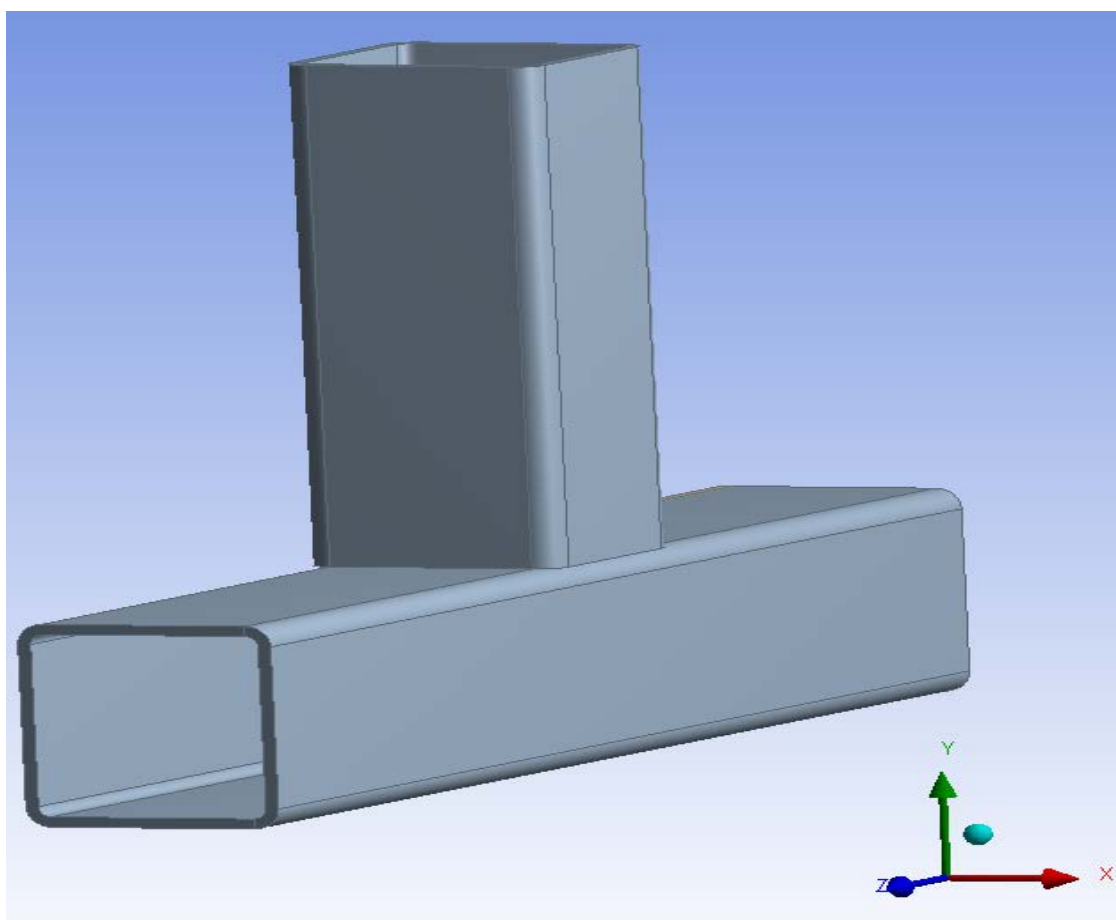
Modelo 3. Vista 3D de la unión en T sin soldadura
